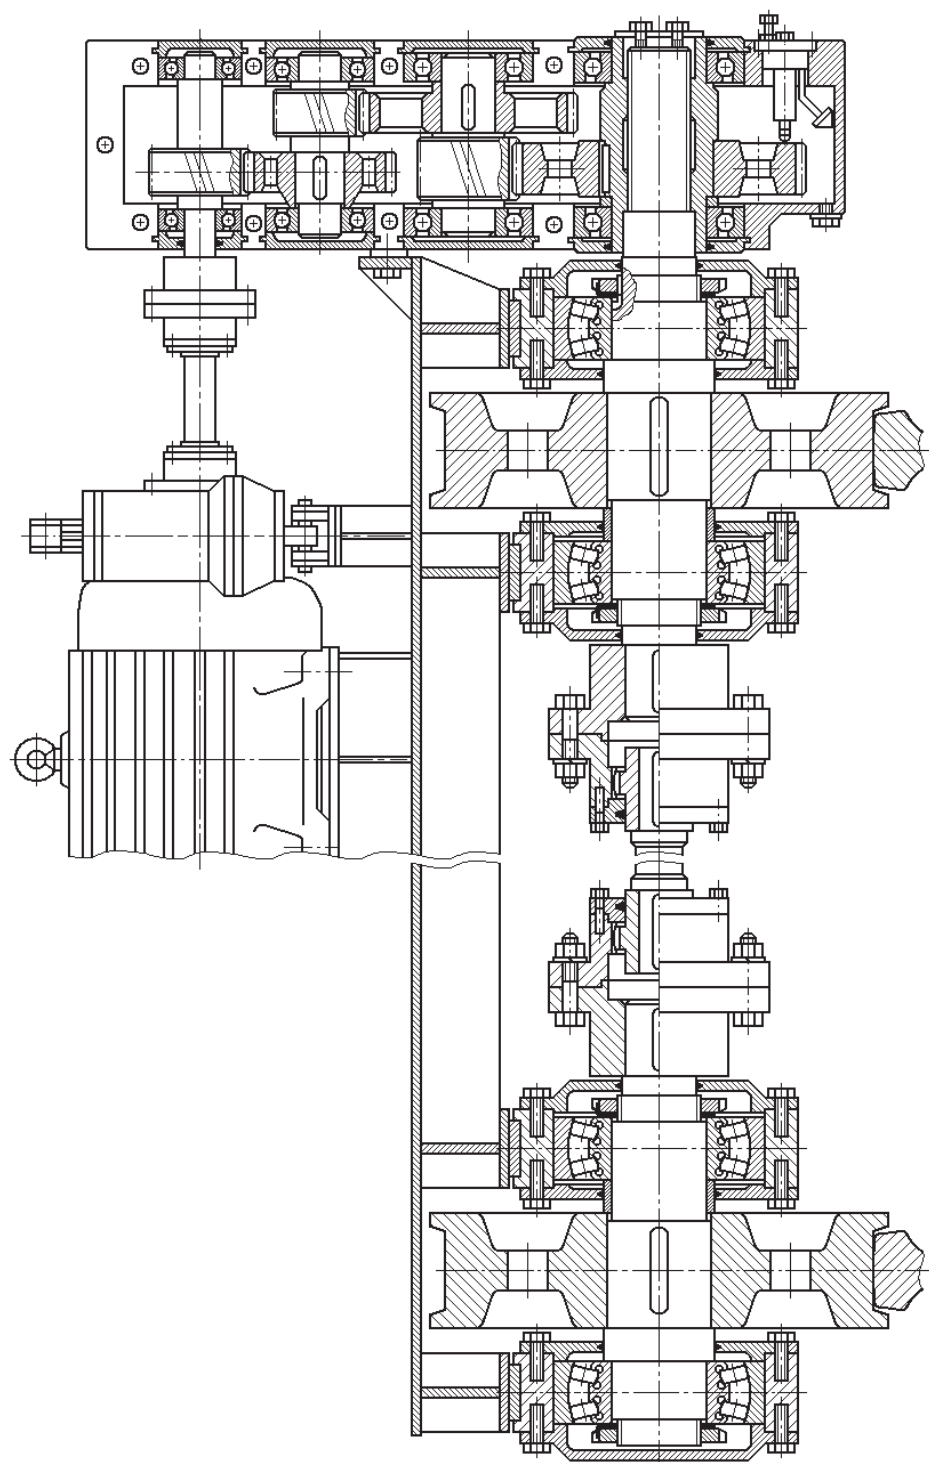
Привод механизма передвижения с навесным редуктором типа ЦЗвк
